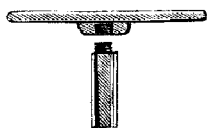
Man nimmt dazu Messingplatten von einer Linie (3 Millimeter) Dide — dünnere biegen sich schon beim Bearbeiten zu leicht — und zwei Zoll
